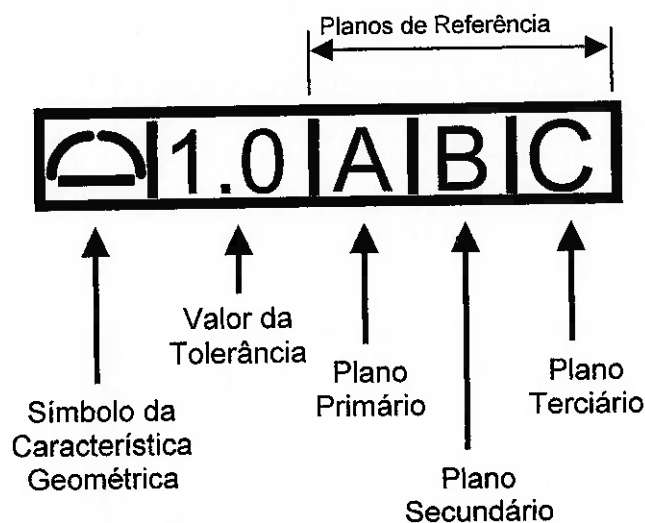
GD&T – Quadro Básico de Controle
